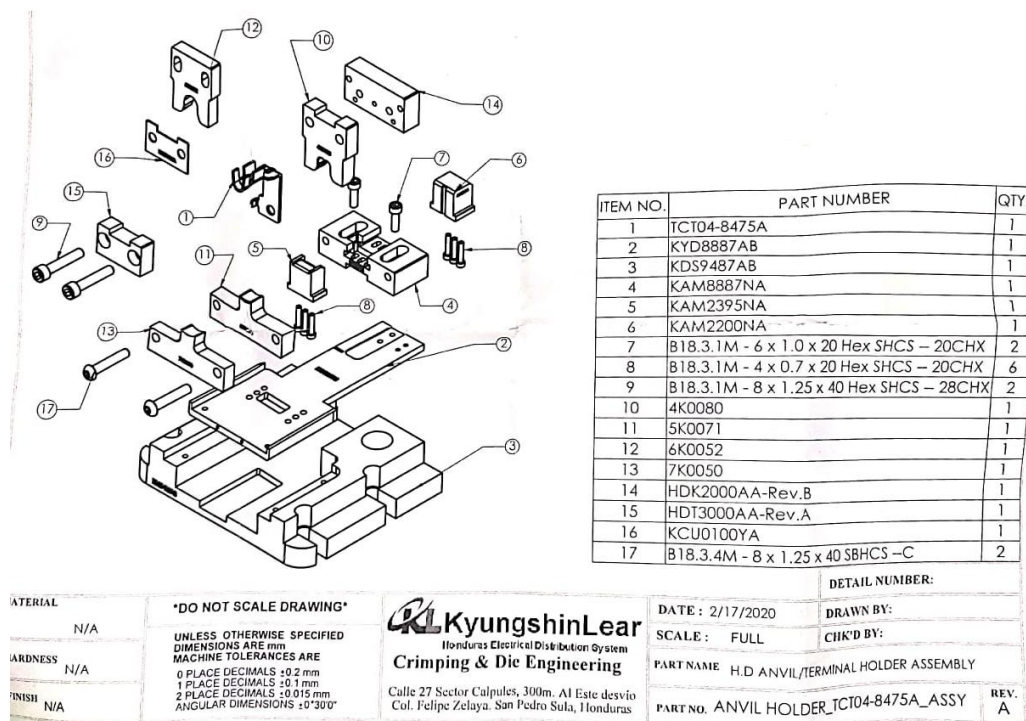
Vista explosionada herramientas especiales de troquel heavy duty
